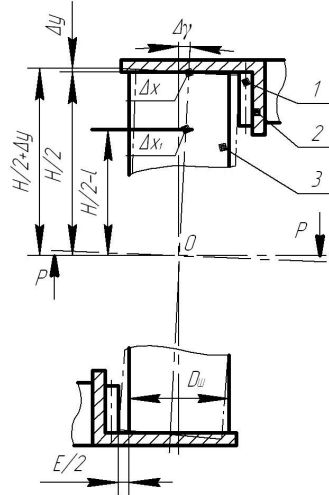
Вплив геометричних параметрів карданного шарніра на нелінійність контакту шипа з голчастими роликами підшипника: 1 – голчастий ролик; 2 – обойма підшипника; 3 – шип хрестовини.
